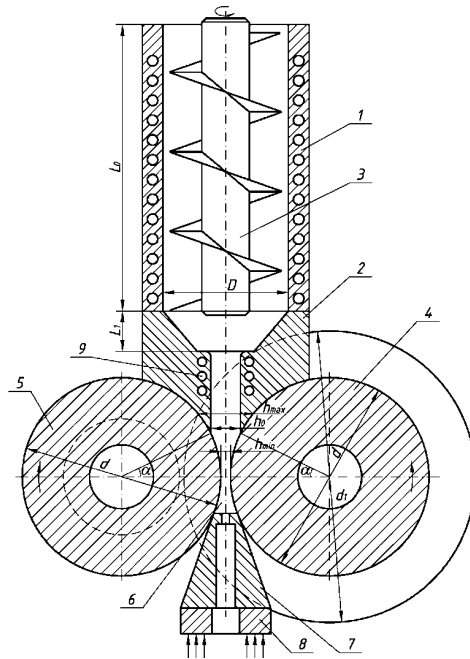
Схема устройства для совмещенной прокатки-прессования пресс-изделий из сыпучей стружки алюминиевых сплавов: 1 – контейнер; 2 – форкамера; 3 – приводной шнек; 4 – валок с канавкой; 5 – валок с выступом; 6 – закрытый калибр; 7 – матрица; 8 – гидropriжим; 9 – нагреватели
